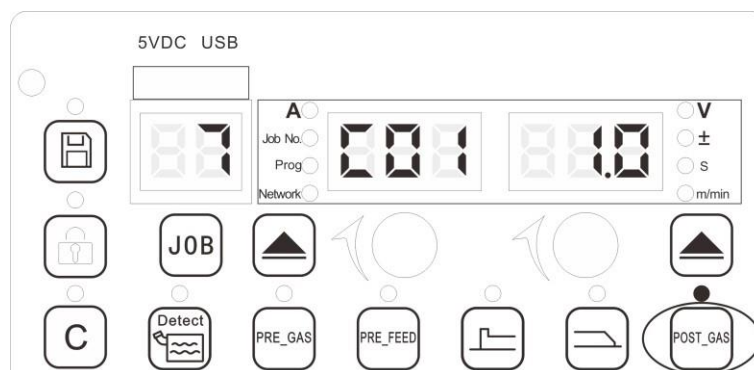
Настройка параметров подачи газа после сварки
